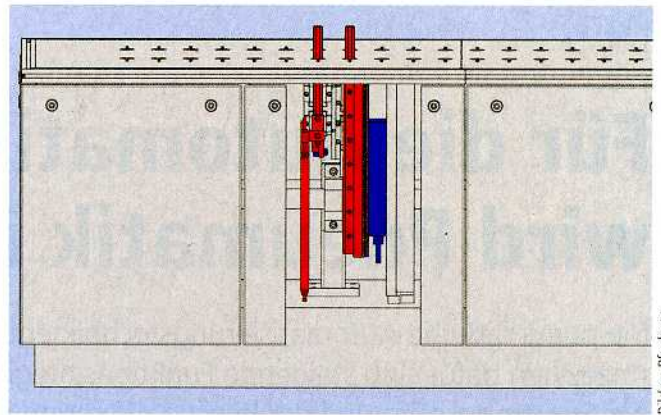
Längstransfersystem (LTS) mit mechanischen und linearmotorischen Antrieben.
